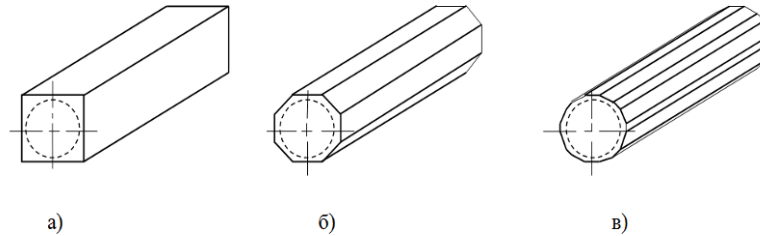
Варіанти профілів заготовок при виготовленні деталей тіл обертання на верстатах з ЧПК.
